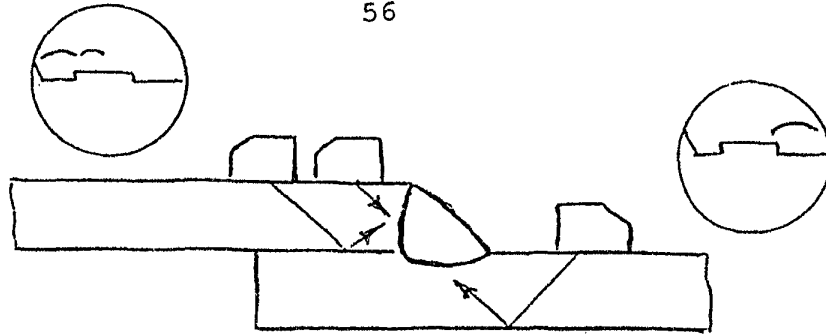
Схемы контроля нахлесточных сварных соединений
